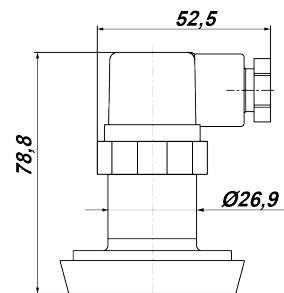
Габаритные и присоединительные размеры ПД180-ДИ, -ДВ, -ДИВ с присоединением молочная муфта DIN 11851
